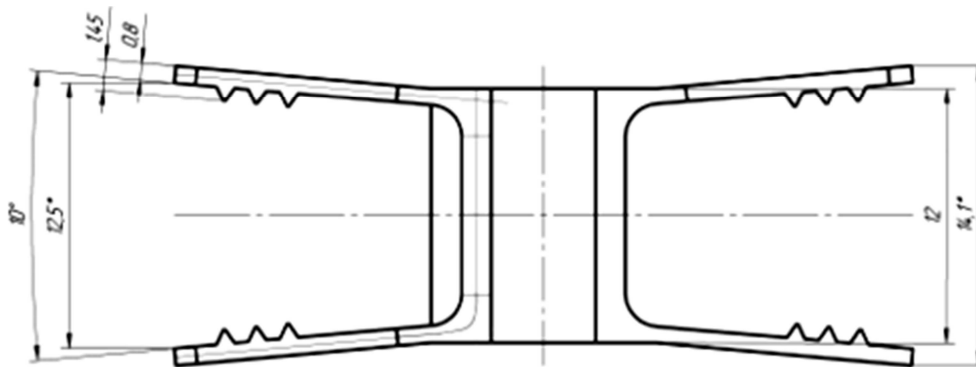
Кресленик деталі «U-імплантат» (вигляд зверху)
